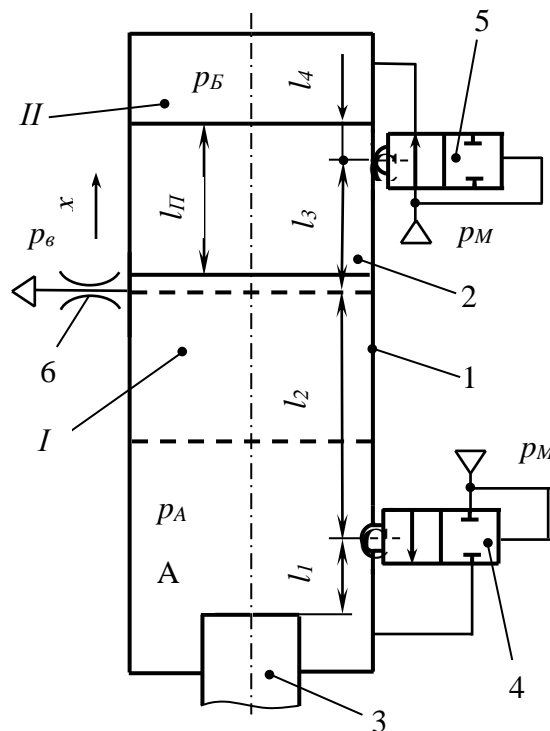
Розрахункова схема пневматичного привода з механічним зв'язком між поршнем-ударником та системою керування його рухом для початкового етапу фази формування рушійного імпульсу:
